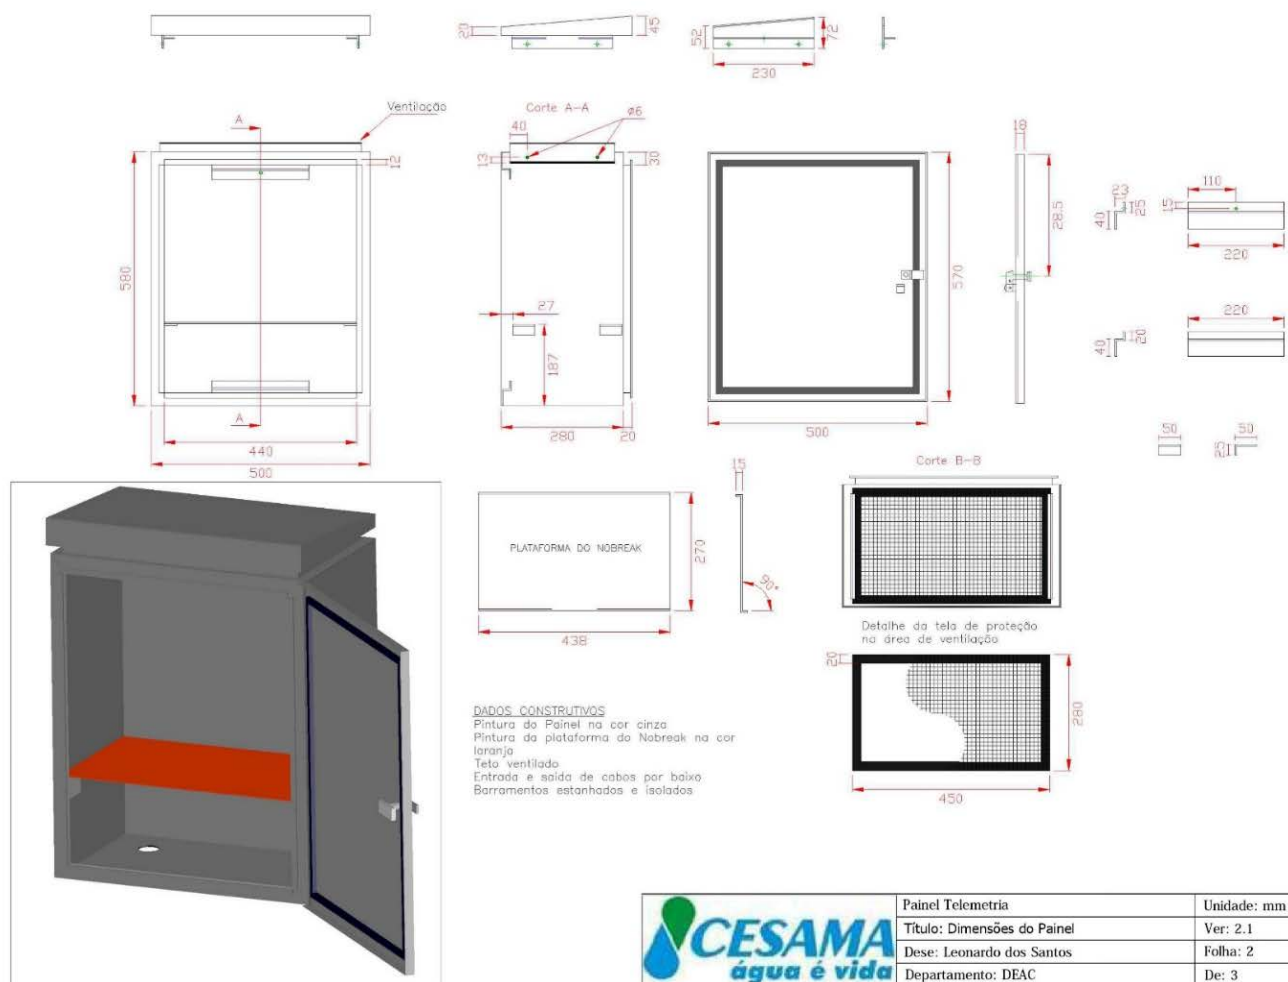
Detalhes construtivos painel de telemetria padrão CESAMA
